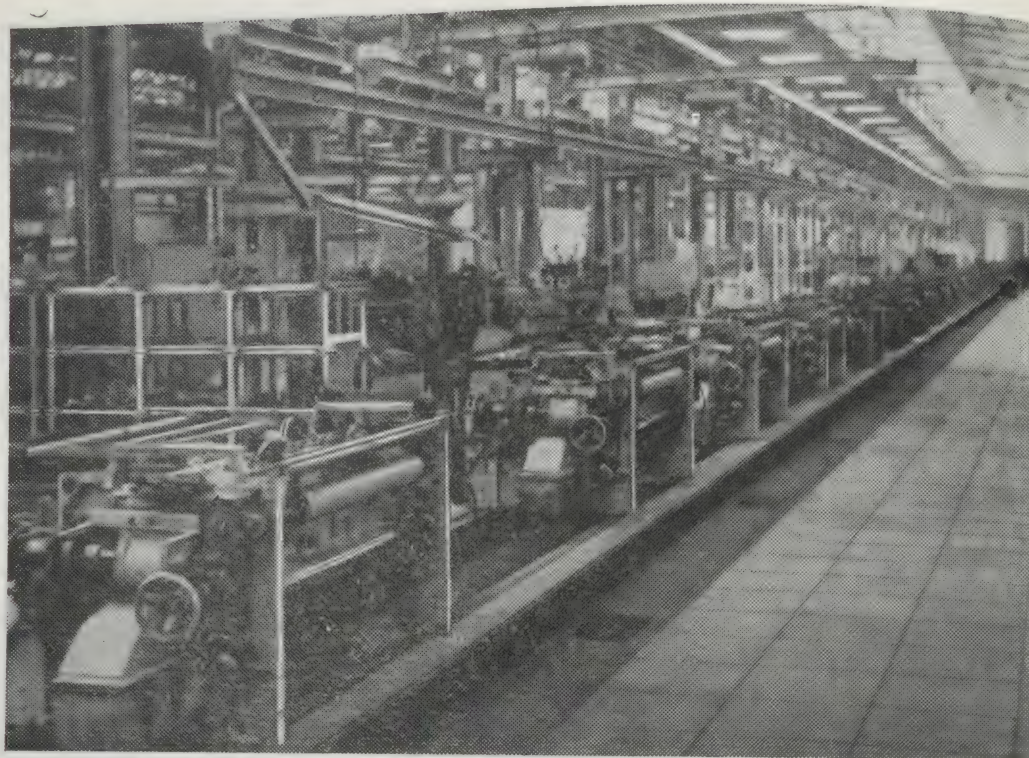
Конвейер окончательной сборки станка АТПР-100
